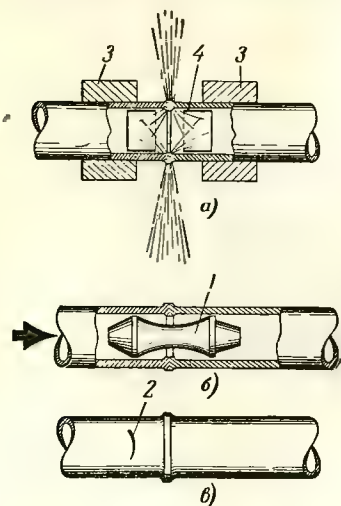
Схема автоматической стыковой сварки труб.
